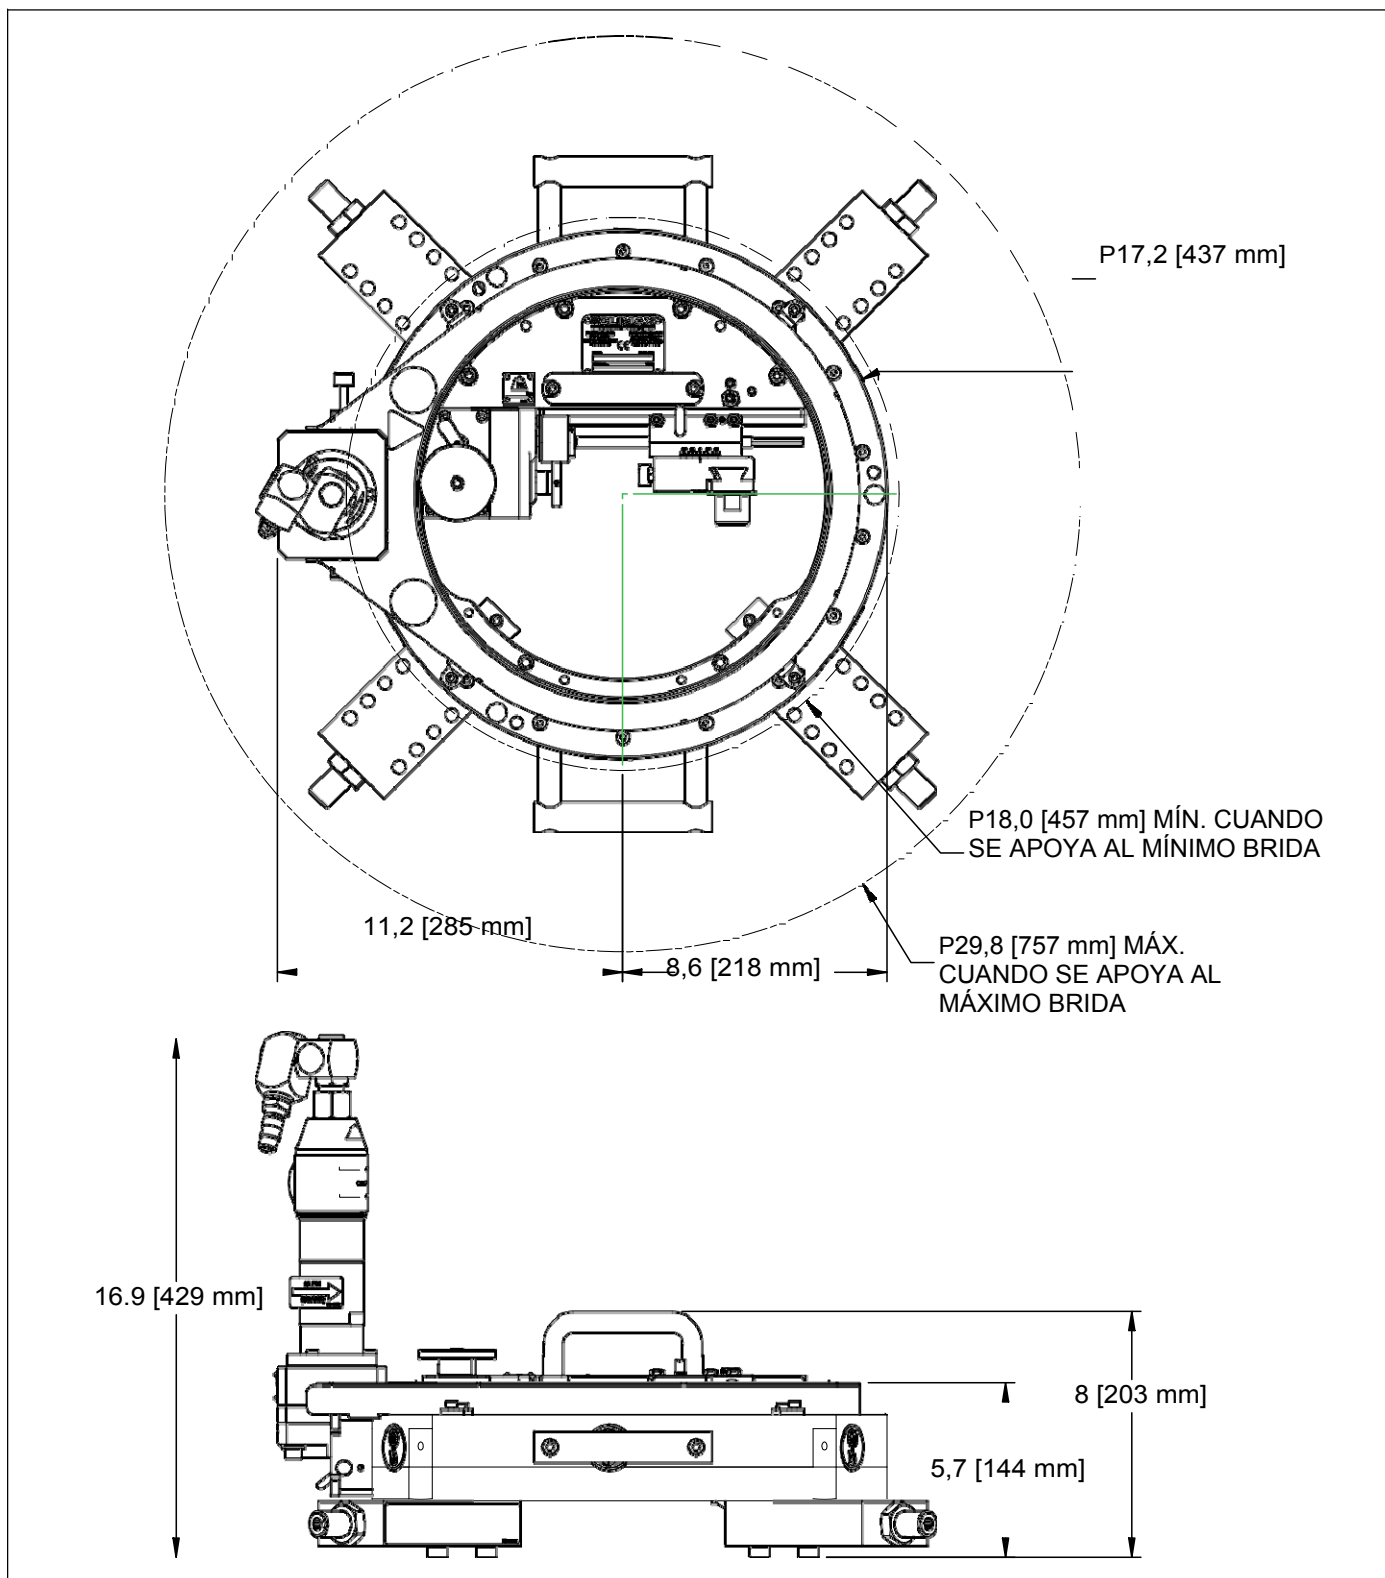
DIMENSIONES DE LA MÁQUINA FF1200
